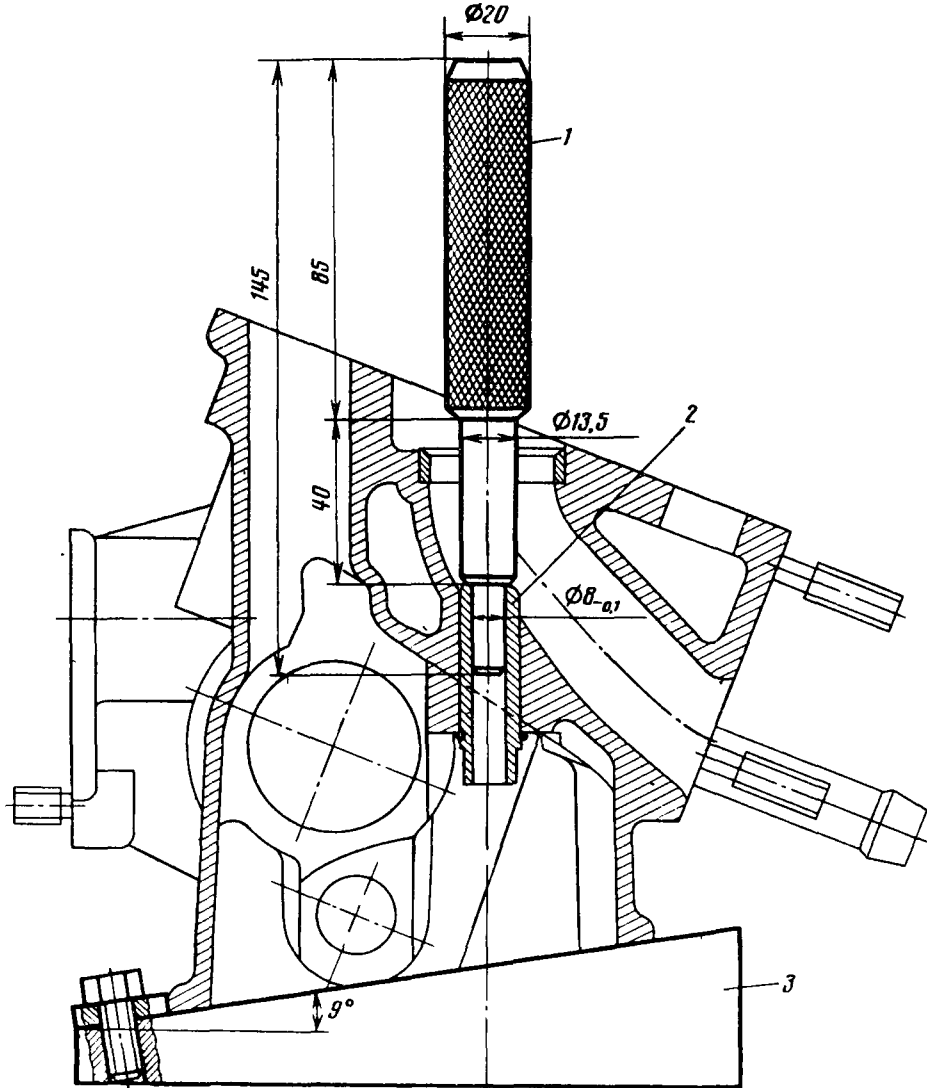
Оправка для выпрессовки направляющей втулки клапана:
